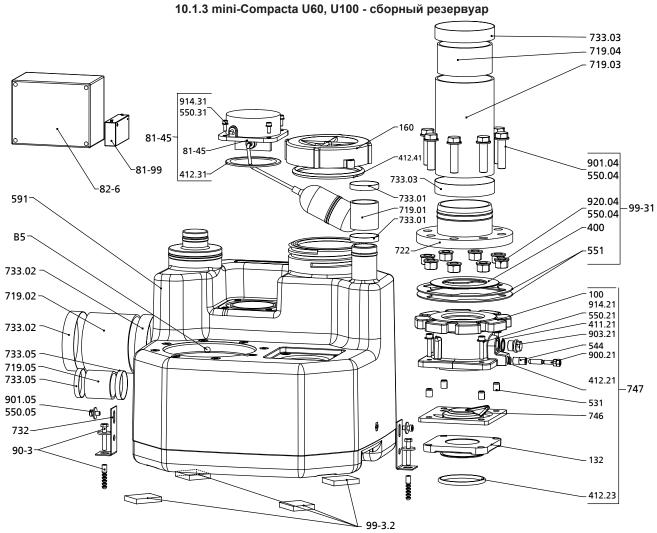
Деталировочное изображение mini-Compacta U60, U100 - сборный резервуар
